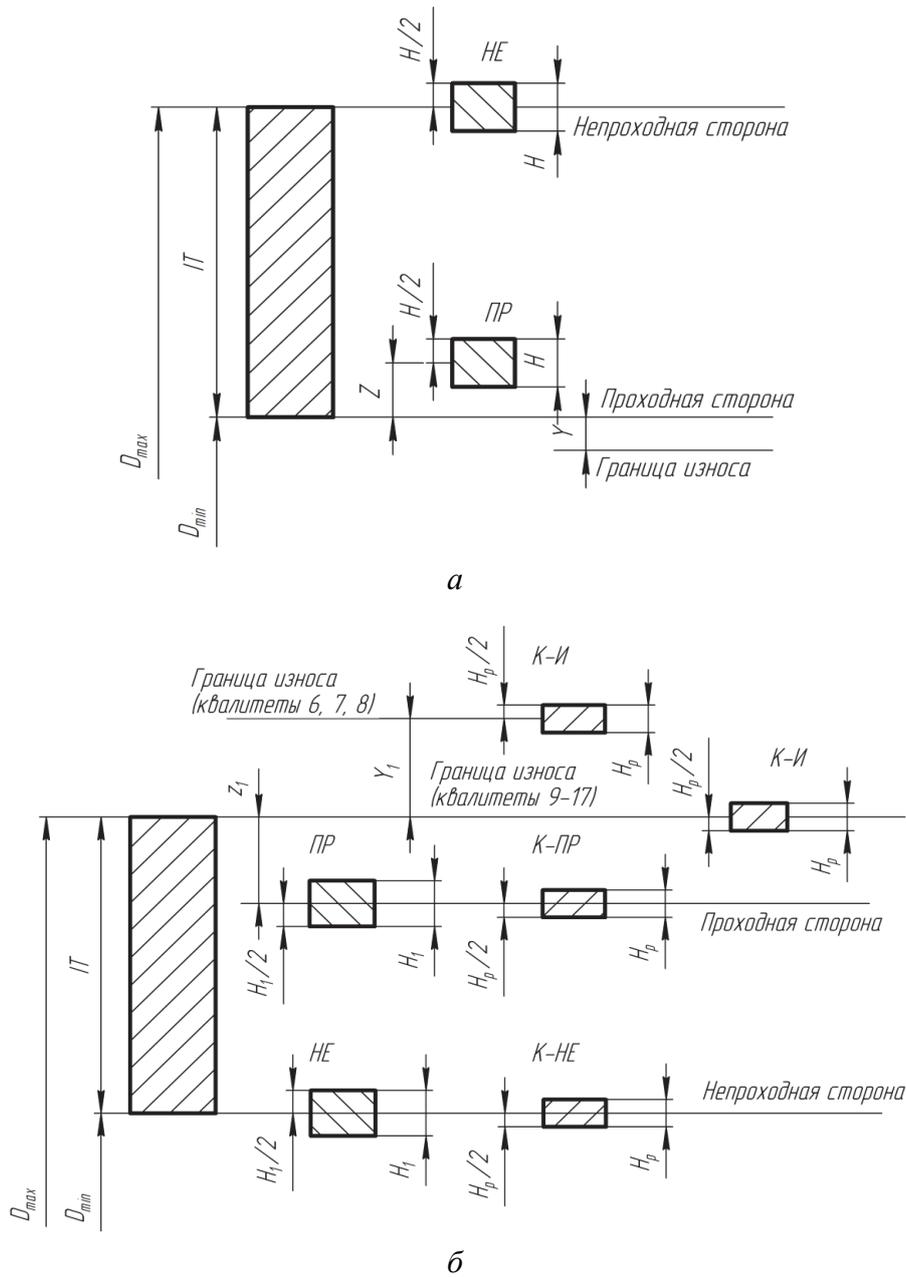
Схемы расположения полей допусков калибров:
